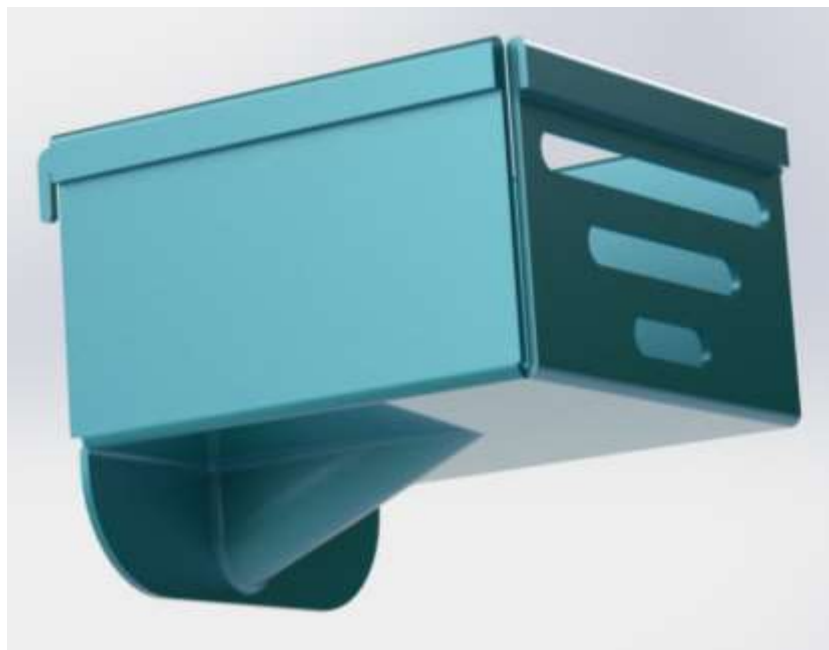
Модель деталі «Підставка», створена інструментами моделювання деталей з листового металу
